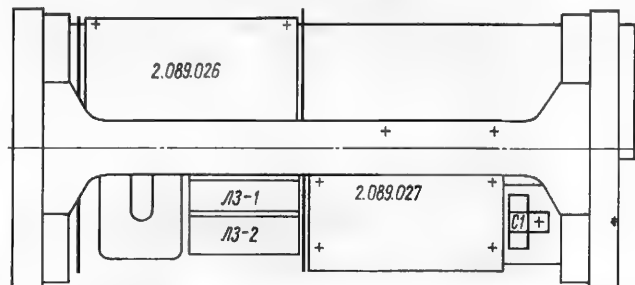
Схема расположения установочных элементов и печатных плат (вид сбоку)
